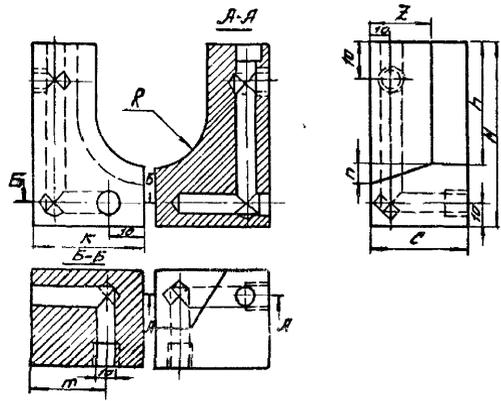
Рабочие чертежи медных форм для сварки втавр одиночных стержней с пластиной при изготовлении закладных деталей типа "открытый" и "закрытый" столлик.
